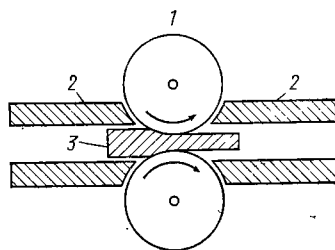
Схема горячей прокатки для изготовления поликристаллического КСl из монокристаллических заготовок: 1 — нагретые валки; 2 — туннельная печь; 3 — заготовка
